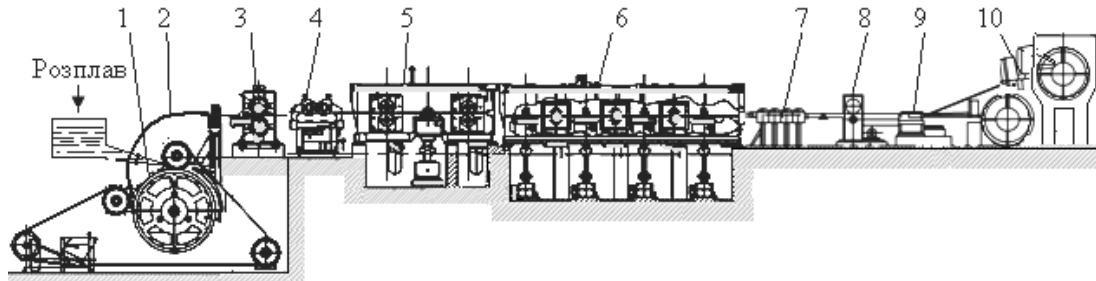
Принципова схема ливарно-прокатного агрегату конструкції «АХК ВНДІ-МЕТМАШ»
